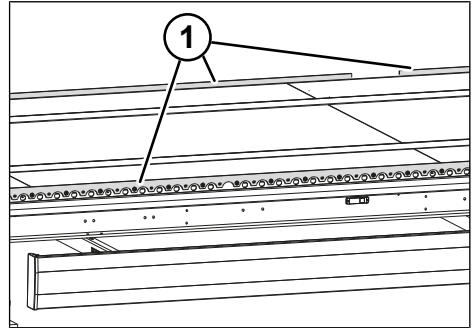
Multi Screw la cadrul exterior Multi Lock
